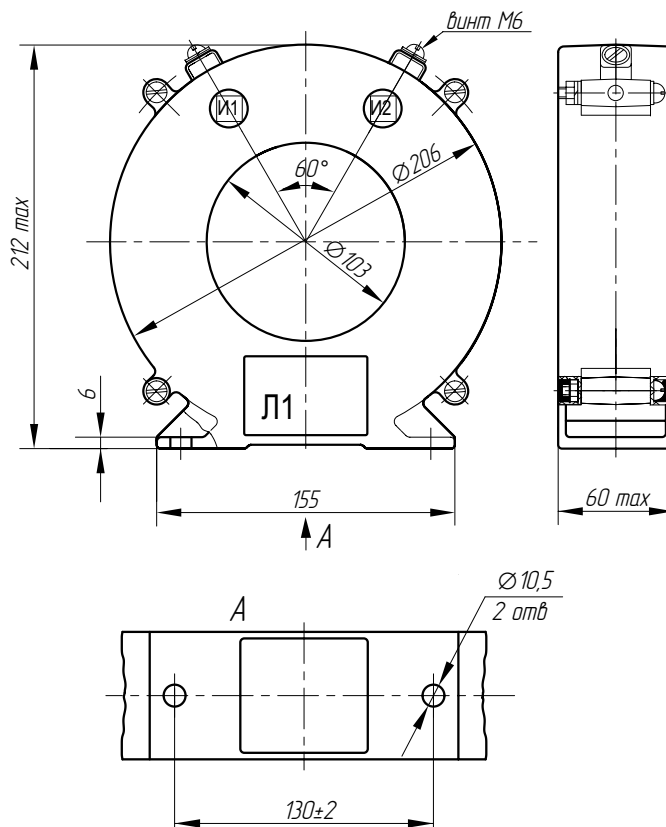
Общий вид трансформатора ТНШЛ-0,66 в пластмассовом корпусе на токи 600–2500 А
